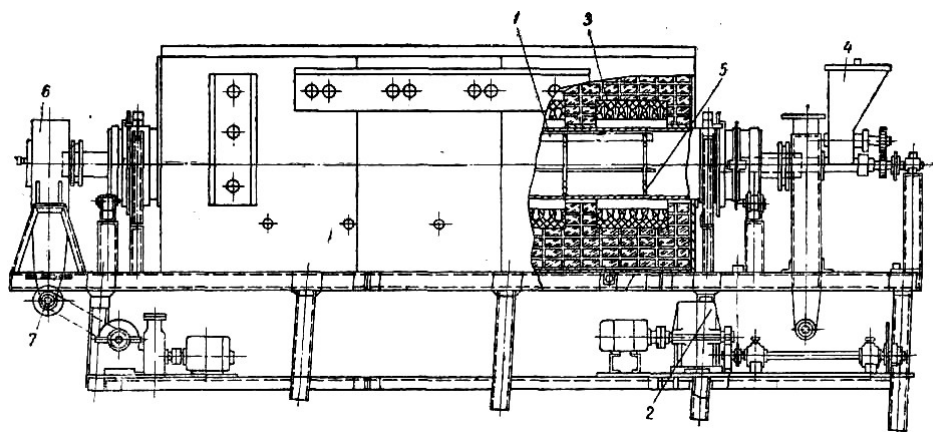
Вращающаяся трубчатая печь для непрерывного восстановления вольфрамового ангидрида водородом: 1 – стальная труба; 2 – привод для вращения трубы; 3 – корпус печи и электронагреватель; 4 – загрузочный бункер с питателем; 5 – стальные дырчатые диски, соединенные уголком; 6 – разгрузочное устройство и место подачи водорода; 7 – механизм для разгрузки
